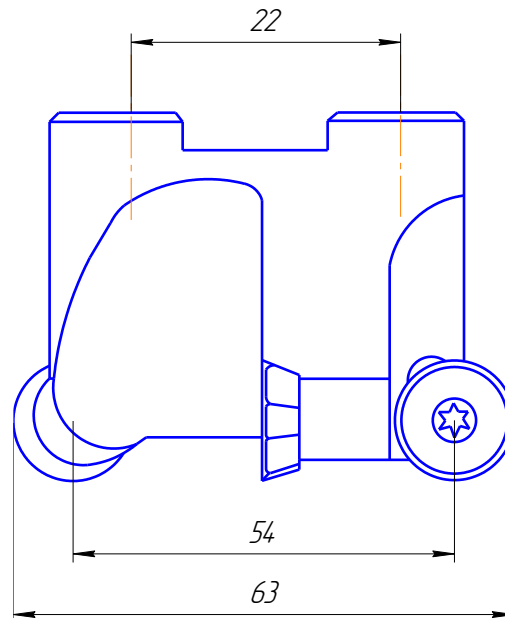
Фреза торцева насадна фірми ISKAR модель FRCM
